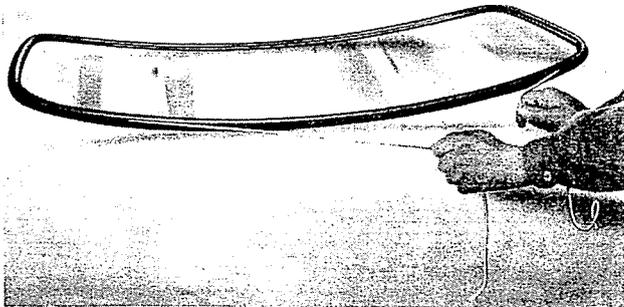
Einlegen der Schnur in die Nute des Gummirahmens der Windschutzscheibe.
